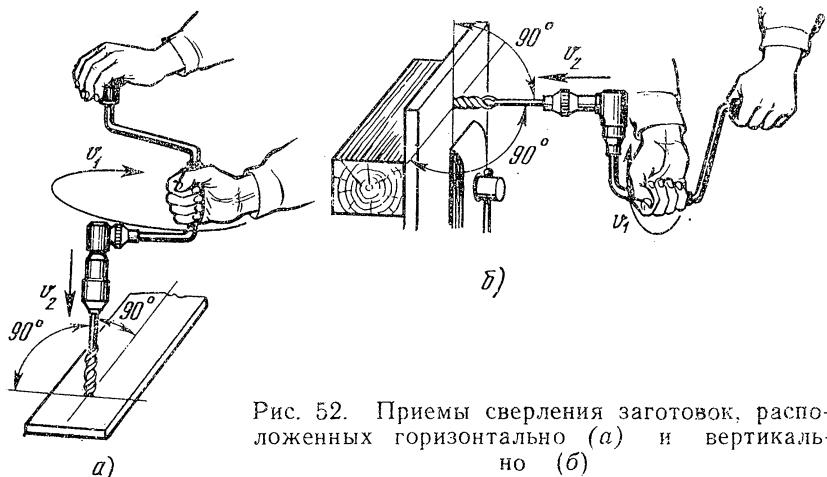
Приемы сверления заготовок, расположенных горизонтально (а) и вертикально (б)
